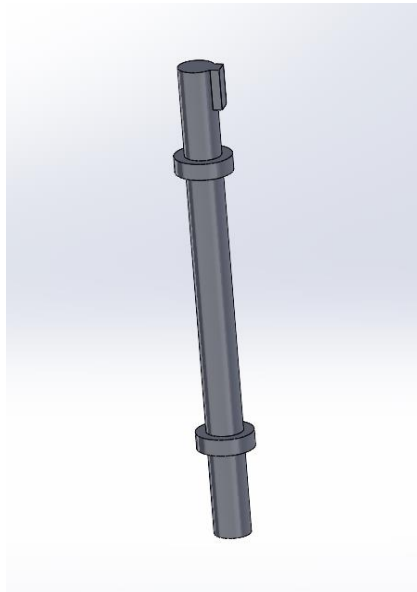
Árbol de Transmisión Motor/Rueda en SolidWorks
